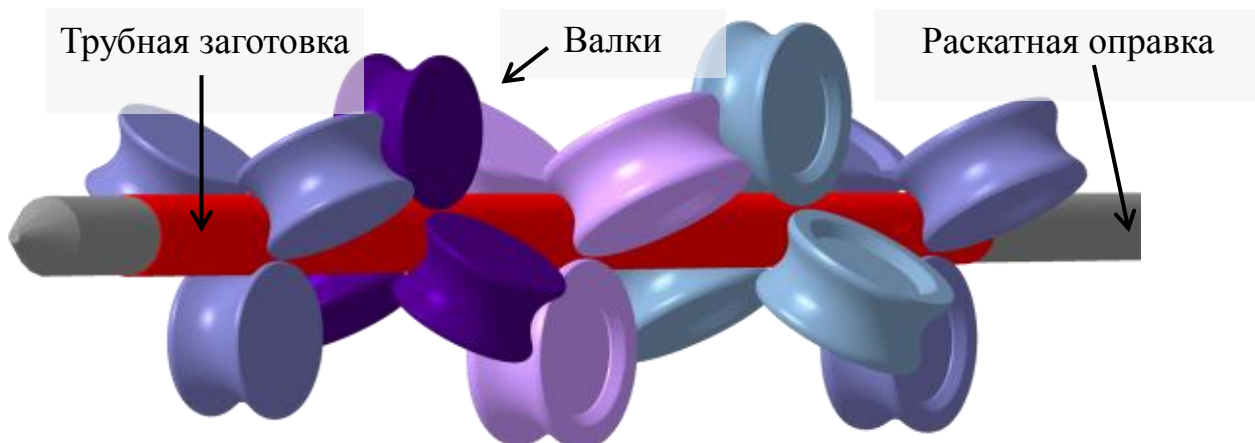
схема раскатки трубной заготовки в стане PQF
